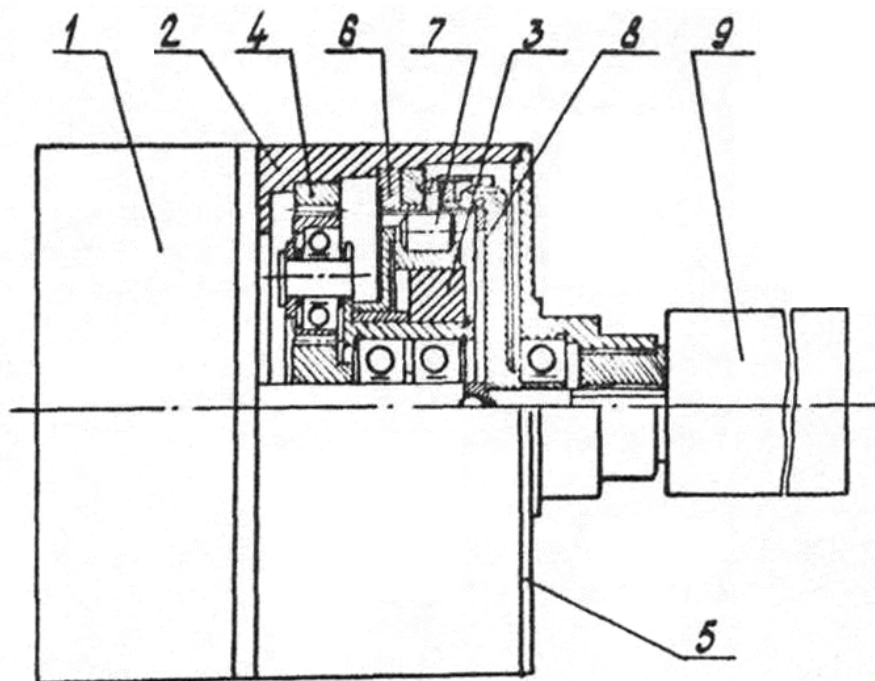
Общий вид привода потенциометра: 1 — электродвигатель; 2 — корпус; 3 — генератор; 4 — планетарная передача; 5 — крышка корпуса; 6 — колесо жесткое; 7 — колесо гибкое; 8 — полу муфта зубчатая; 9 — потенциометр.
